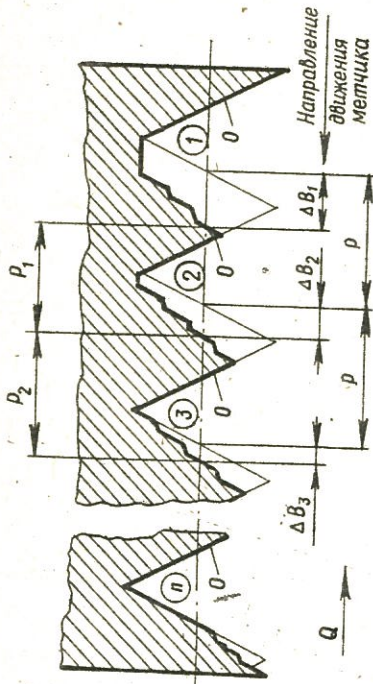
Искажение профиля резьбы под действием осевых сил Q (1, 2, ..., n — впадины нарезанной резьбы; жирной линией показан действительный профиль резьбы)
